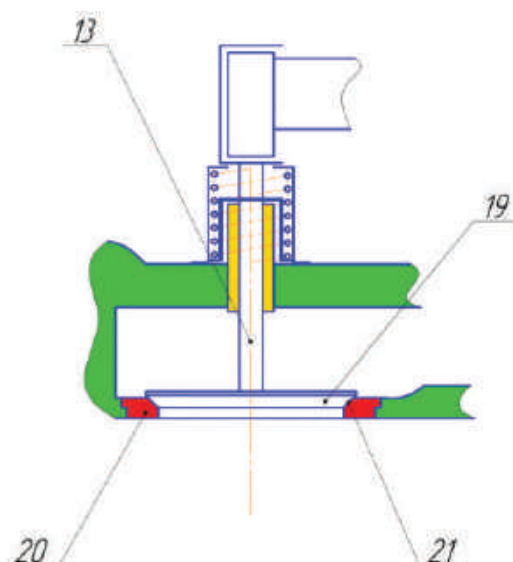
Запорный клапан (13): 19 – опорная фланка; 20 – седло клапана; 21 – посадочный пояс
